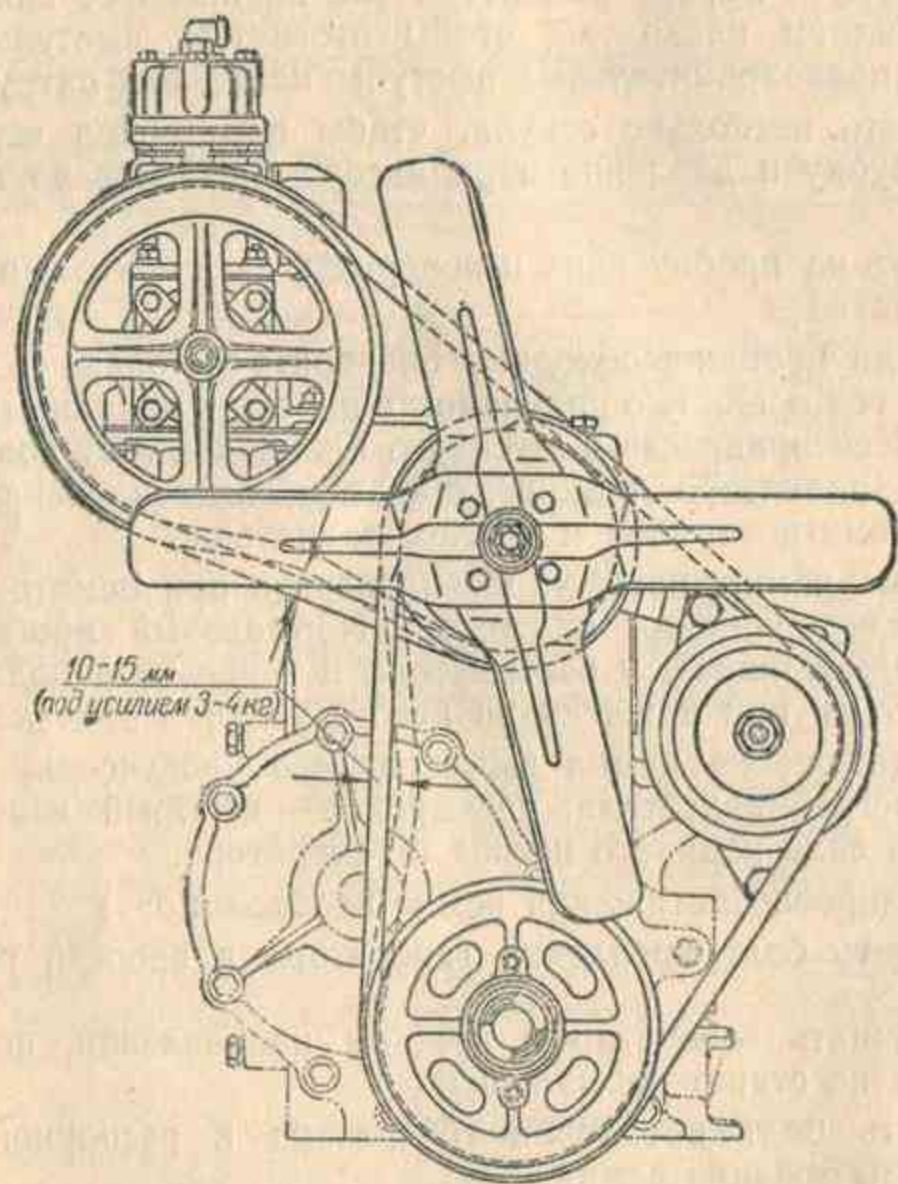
Проверка натяжения ремней привода вентилятора и компрессора
